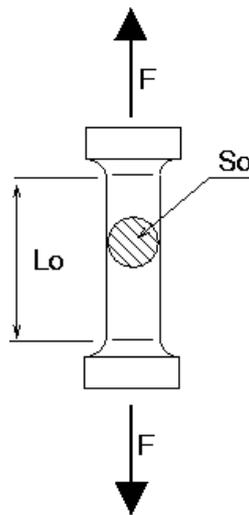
III Dimensions caractéristiques de l'éprouvette.
